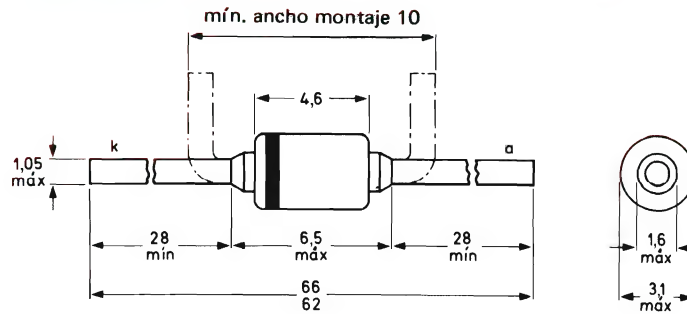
Dimensiones (en mm) del encapsulado SOD-51.
